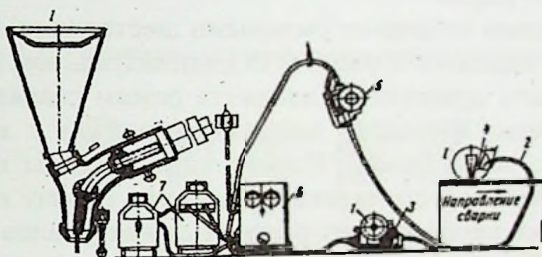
Полуавтомат для сварки под флюсом:
